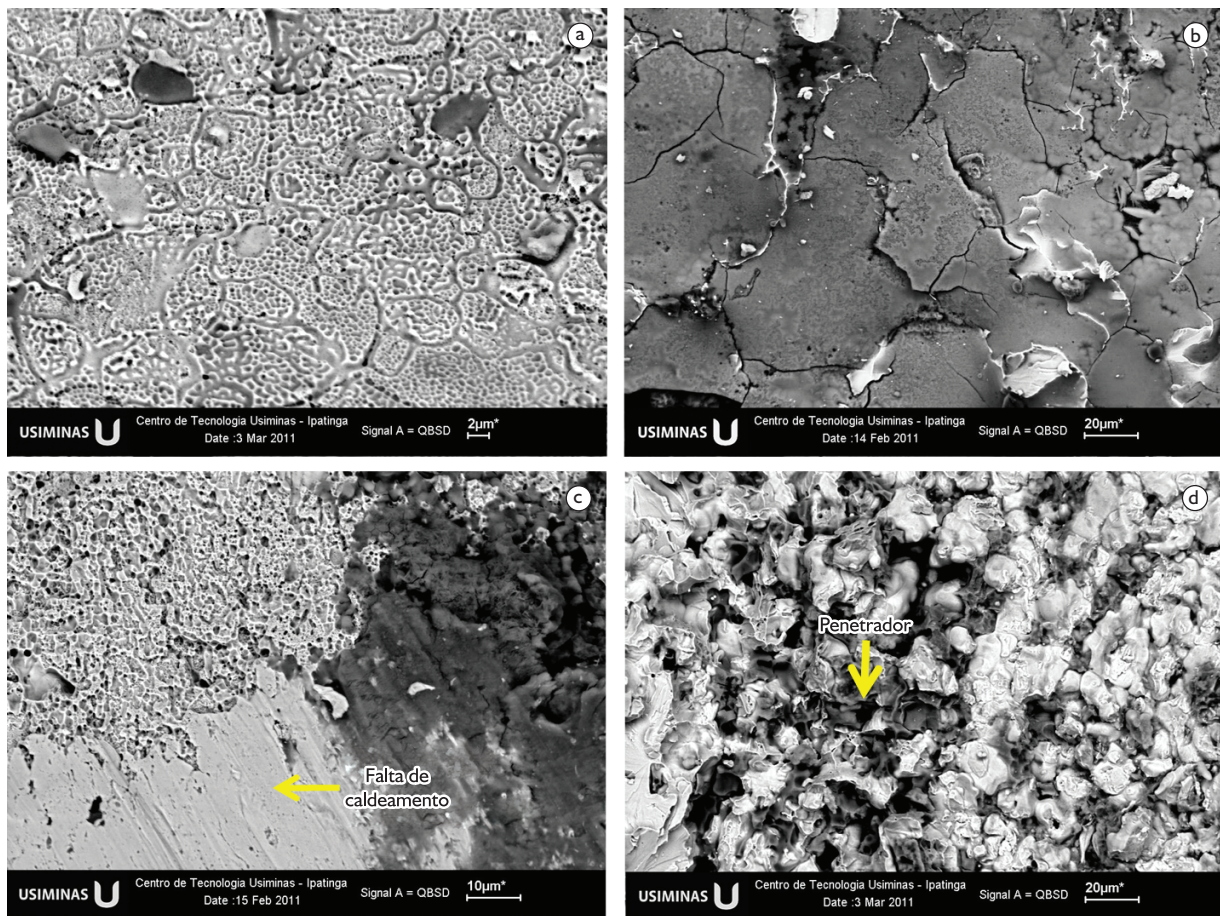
Defeitos observados na superfície de fratura da região de solda de tubos de aço alto silício: (a) solda fria; (b) filme de óxido; (c) falta de caldeamento, em região com os defeitos solda fria e filme de óxido; e (d) penetrador.
